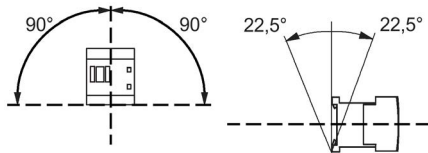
Einbaulagen Baugröße S6, S10, S12
